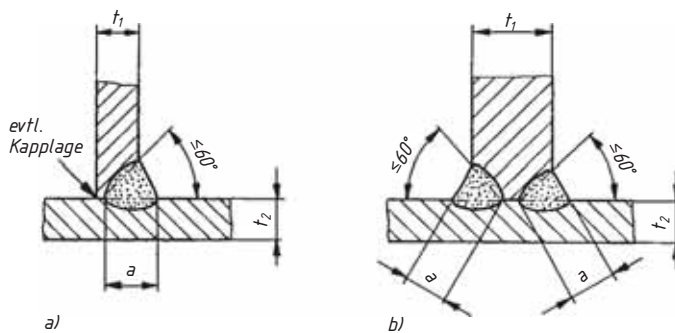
Sonstige Nähte mit nicht durchgeschweißter Wurzel
